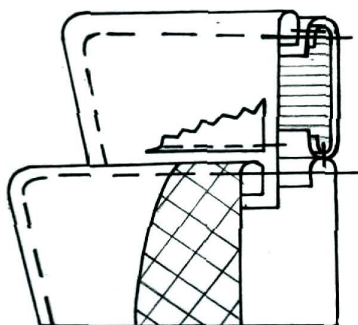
Сборочная схема обработки воротников в изделиях из толстой кожи
